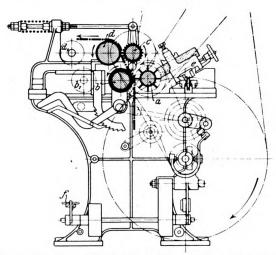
Streck- und Entfleischmaschine mit Transportwalzen. a Messerwalze. b Gummiwalze. c Transportwalze mit Riffeln. d Transportwalze mit Gummibezug. e Schleifapparat. f Fußtritt zum In- und Außerbetriebsetzen der Transportwalzen. b und d, Stallungen der Walzen b und d, um das Werkstück in die Maschine einzulegen.
